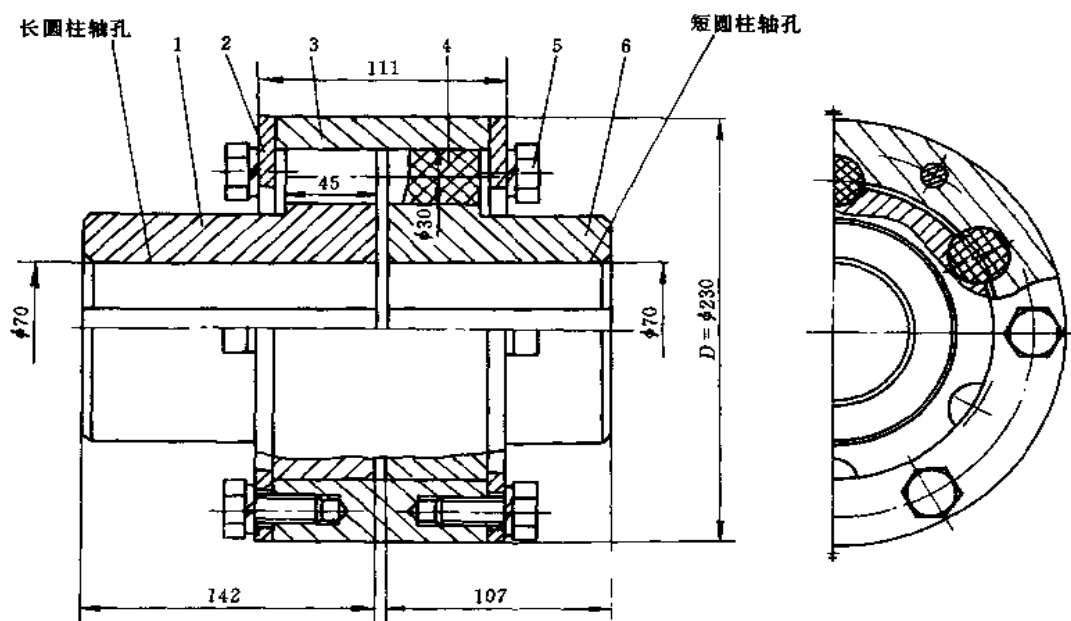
弹性柱销齿式联轴器 (ZL 型)
